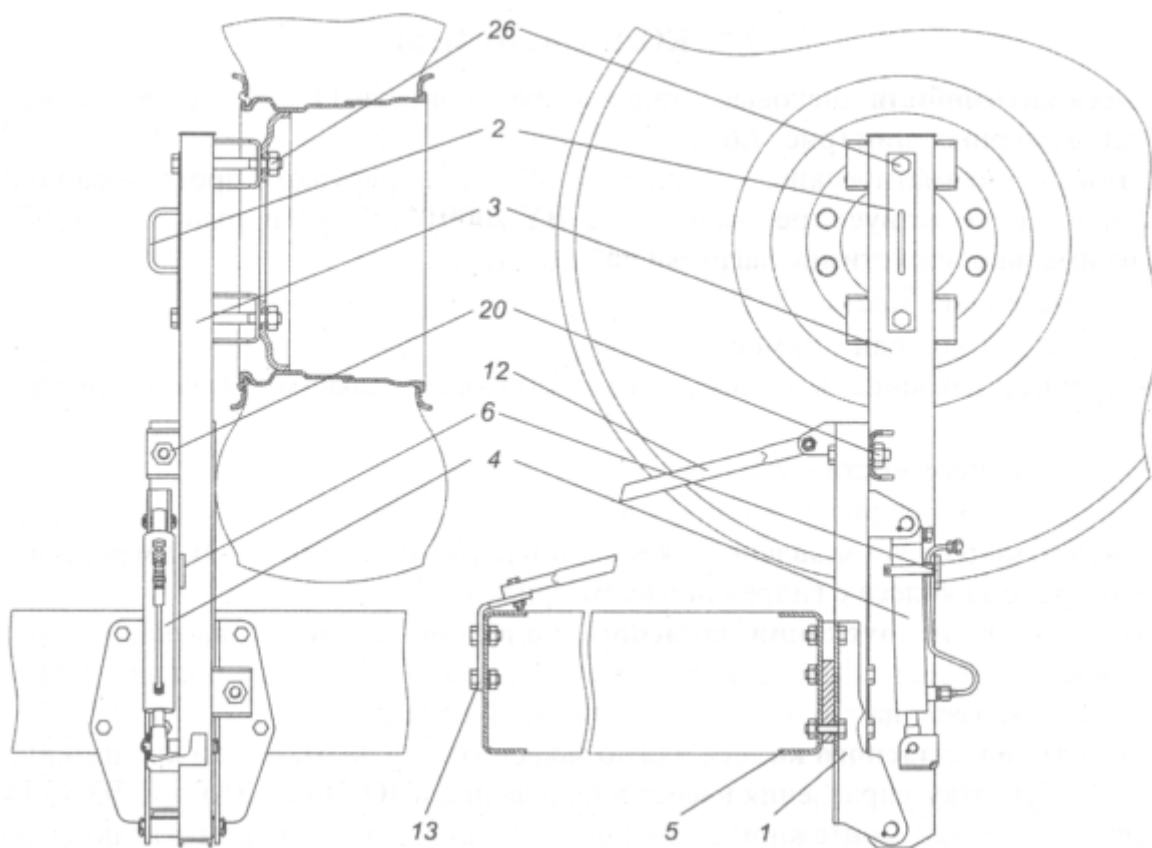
Держатель запасного колеса: 1 - стойка; 2 - пластина с болтами; 3 - стойка откидная; 4 - гидроцилиндр; 5 - правый лонжерон рамы; 6 - направляющая пластина; 12 - стяжка; 13 - кронштейн стяжки; 20, 26 - гайка.
